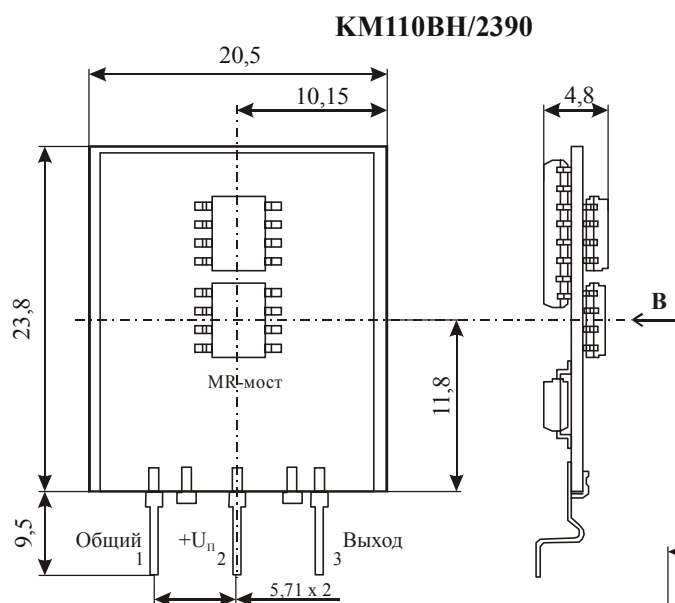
Внешний вид и габаритные размеры датчика типа КМ110Н/2390
